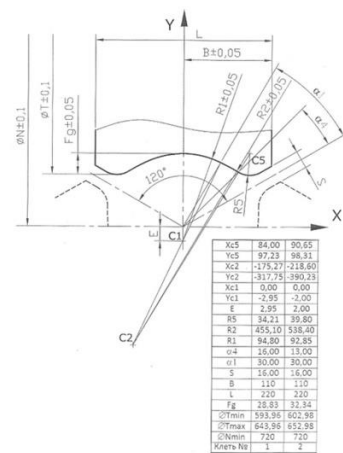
Калібровка валків стану PQF «184», використана для креслення інструменту при моделюванні
